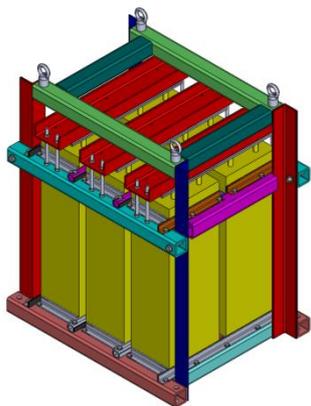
Внешний вид устройства СА-У.
